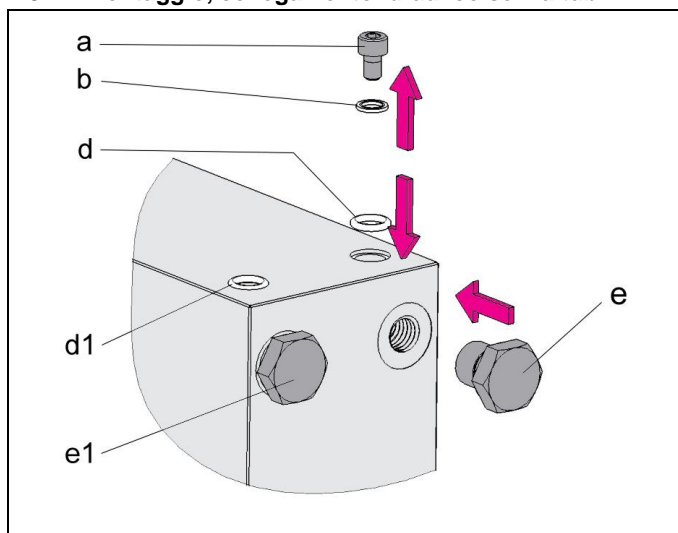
Esempio, installazione della versione a flangia (senza tubi)
